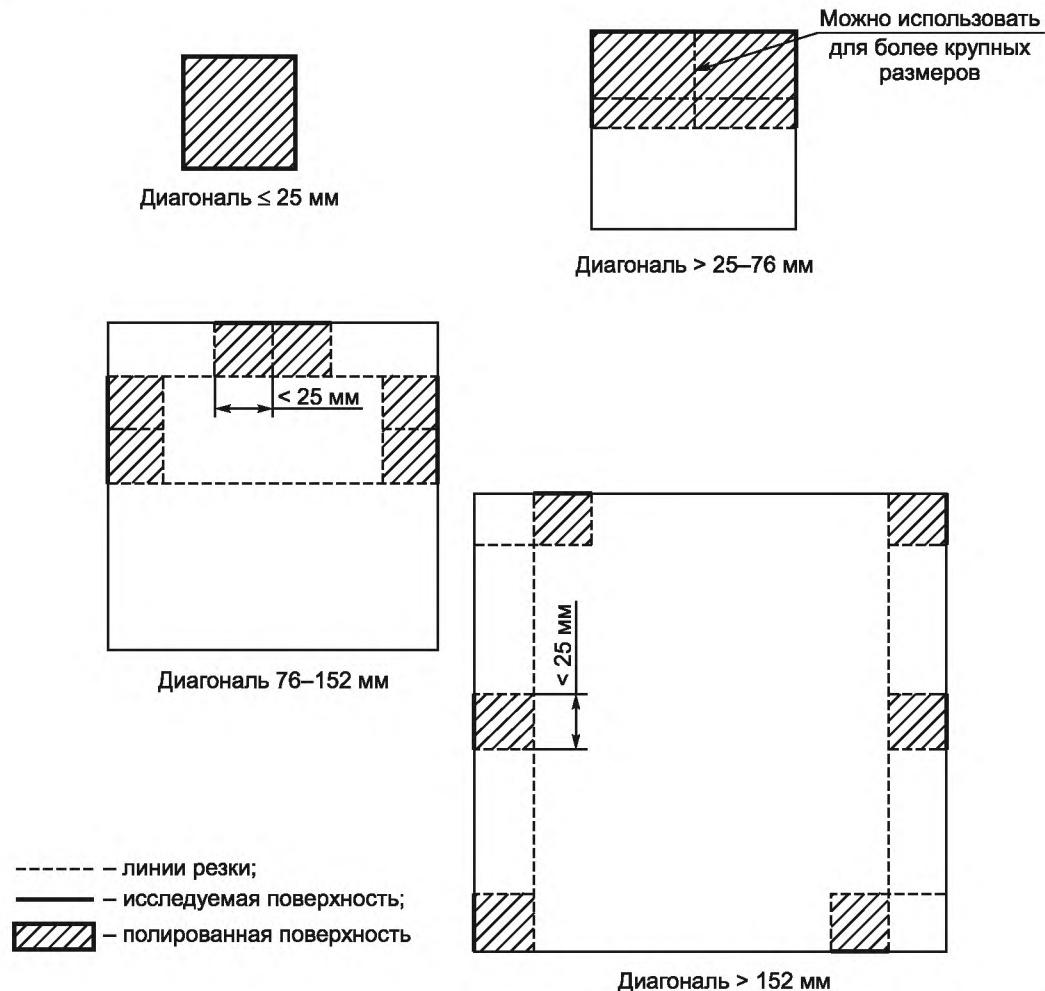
Типичные схемы отбора образцов для квадратных прутков различного размера
